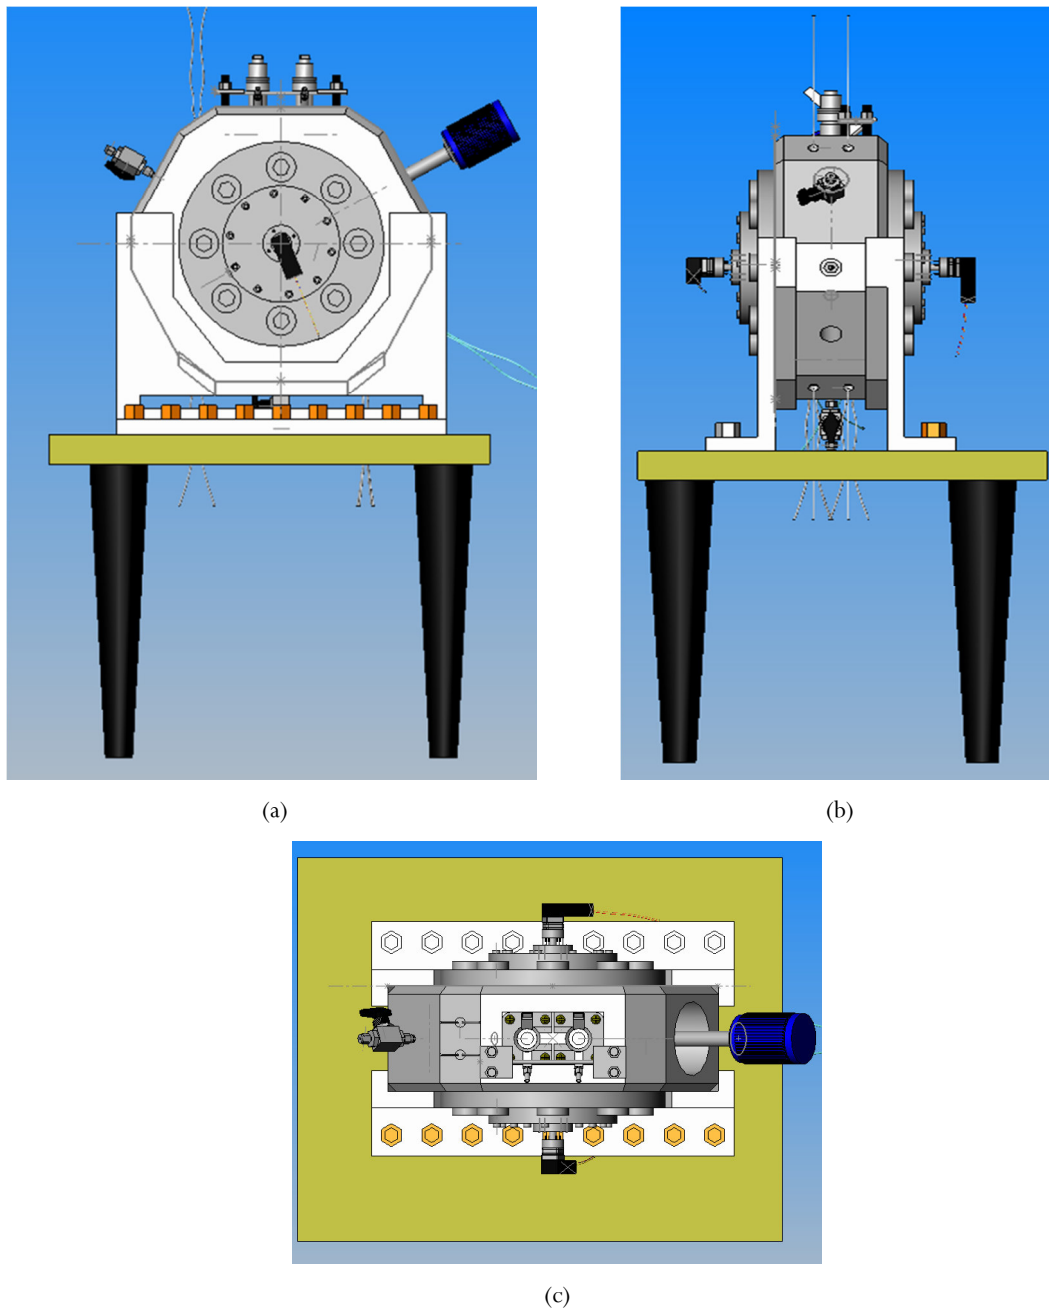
Alzado (a), perfil (b) y planta (c) de la nueva instalación
